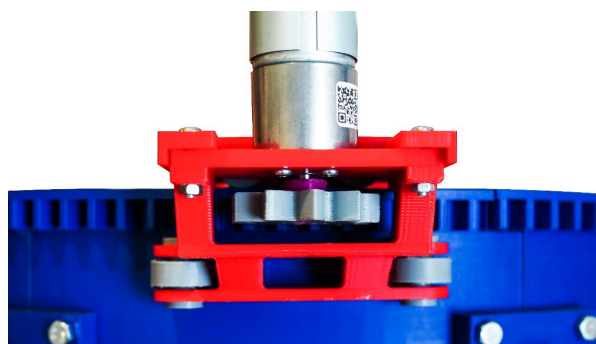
Сборочный узел каретки с приводом и зубчатым колесом, входящим в зацепление с зубьями круговой направляющей
